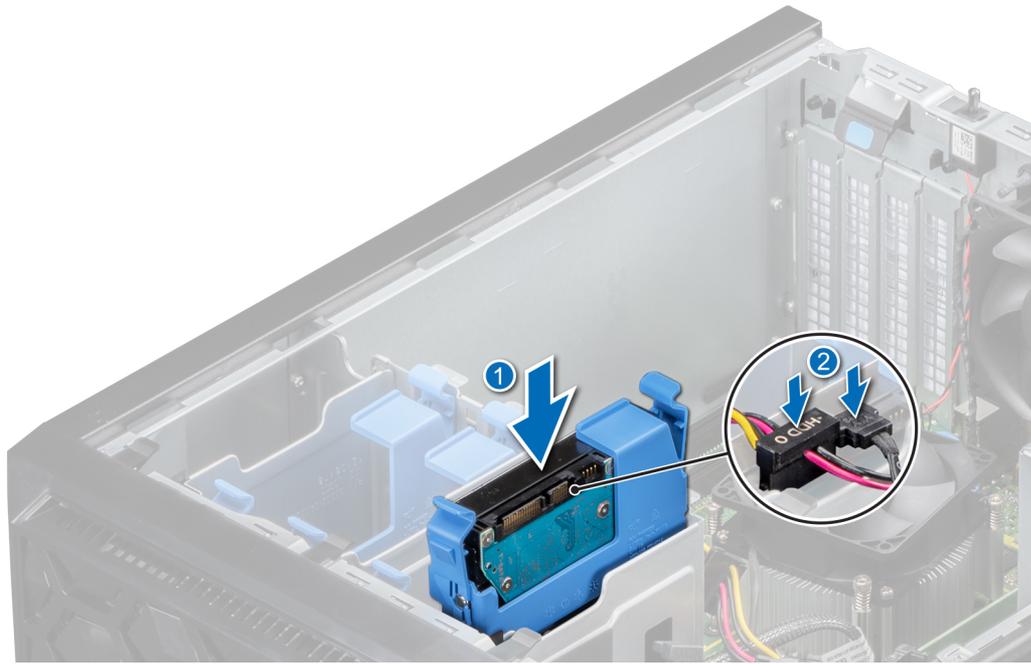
Installieren eines Laufwerksträgers im Laufwerksschacht
